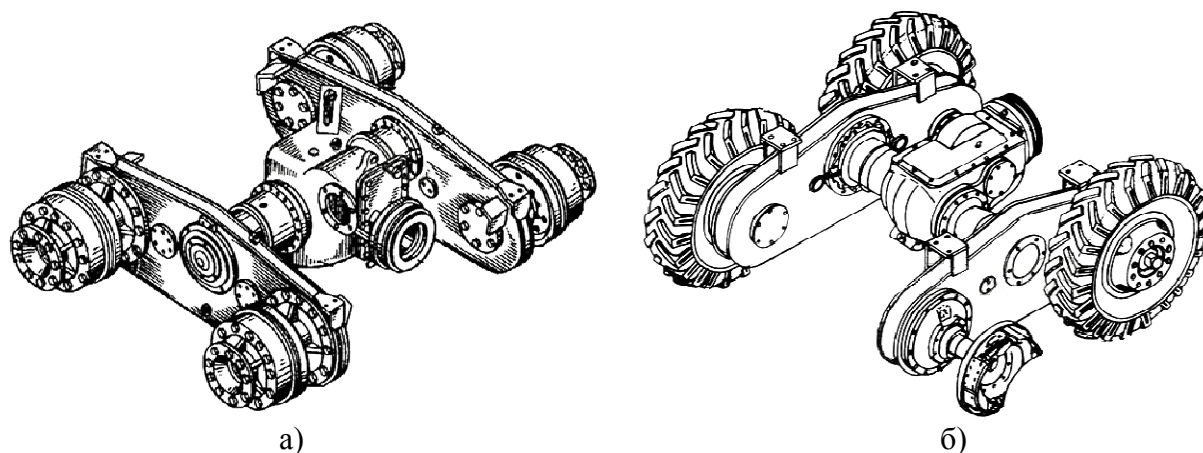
Блокированный балансирующий колесный движитель автогрейдера
